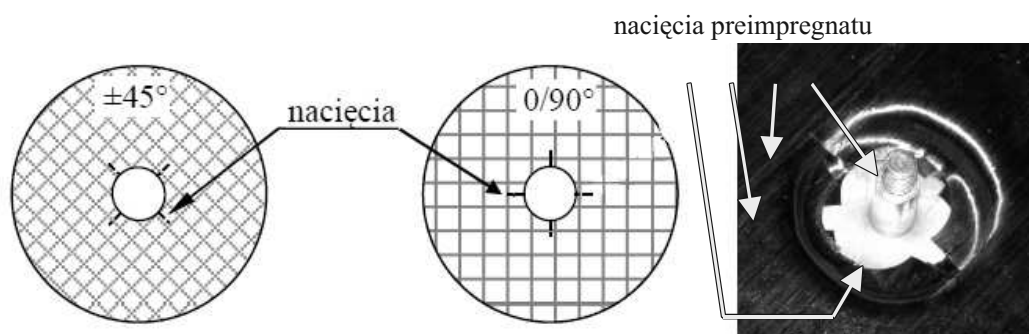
Foremnik z okładziną uchwytu kołowego i pierścieniem BPMK gotowy do wykonywania struktury kompozytowej elementu badawczego
